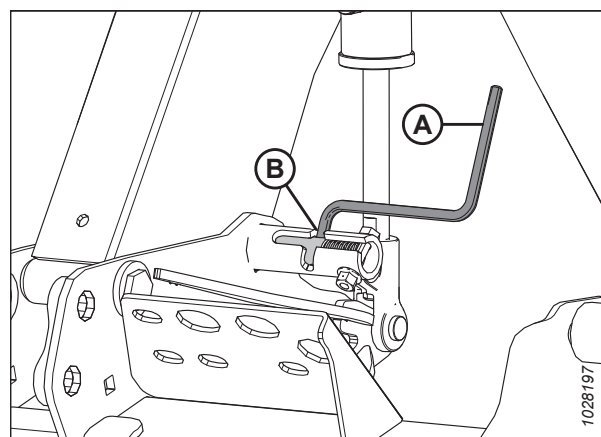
Предохранительный упор мотовила — центральный рычаг
